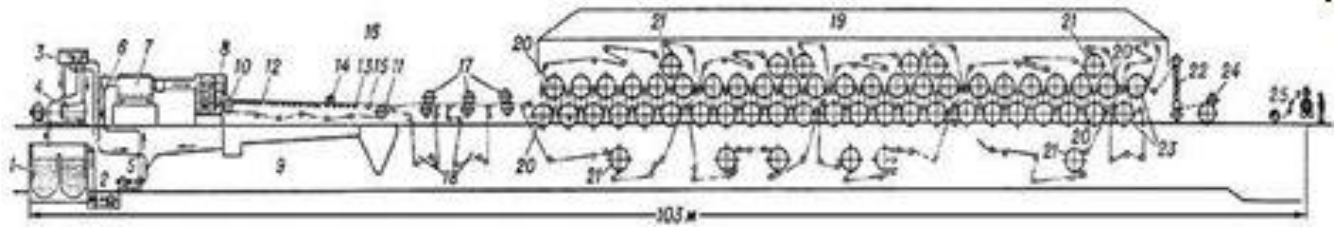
Схема плоскіточної папероробної машини: 1 — машинний басейн; 2 — насос; 3 — бак постійного натиску; 4 — конічний млин; 5 — насос змішувача; 6 — засувки; 7 — очисна апаратура; 8 — напірний ящик; 9 — сіткова частина; 10 — грудний вал; 11 — гауч-вал; 12 — реєстрові валики; 13 — відсмоктуючі ящики; 14 — вирівнювальний валик (егутер); 15 — правильний валик; 16 — пресова частина; 17 — валикові преси; 18 — вовняні сукена; 19 — сушильна частина; 20, 21 — сушильні циліндри; 22 — каландр; 23 — холодильний циліндр; 24 — накат; 25 — подов-жньо-розрізний верстат.
